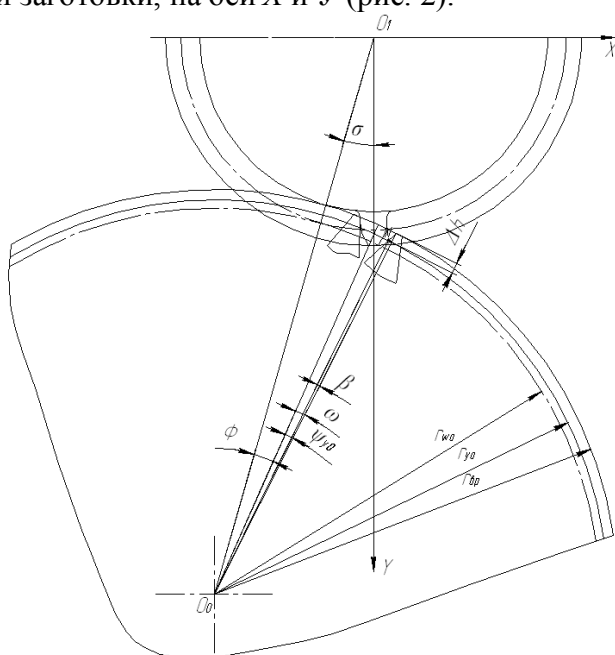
Схема определения положения режущих кромок резцов относительно зуба колеса
